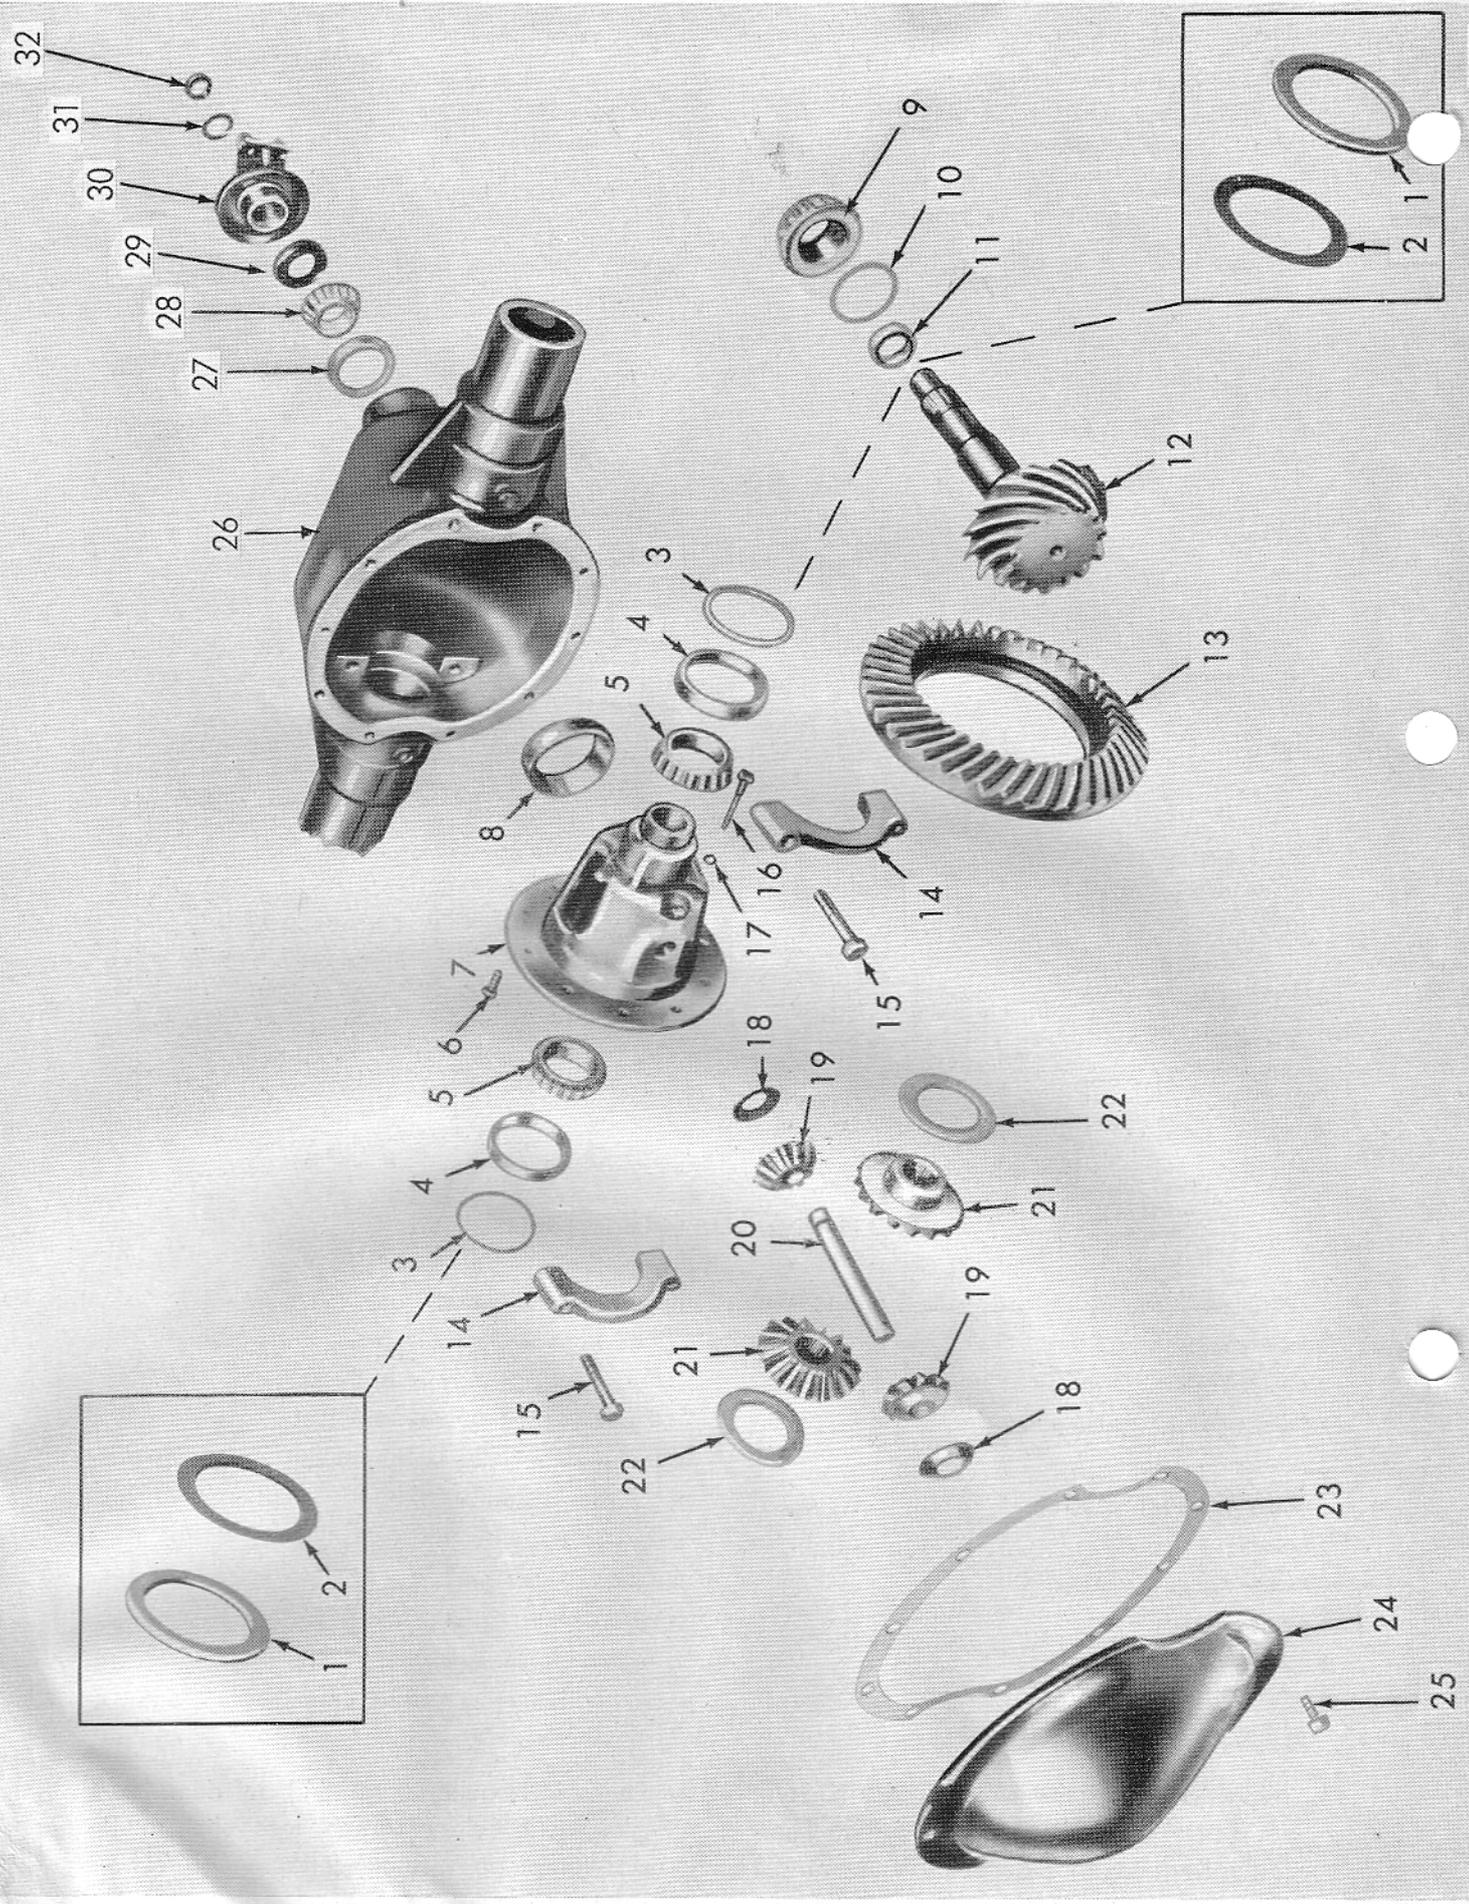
Hinterachsgetriebe - Explosionsansicht
